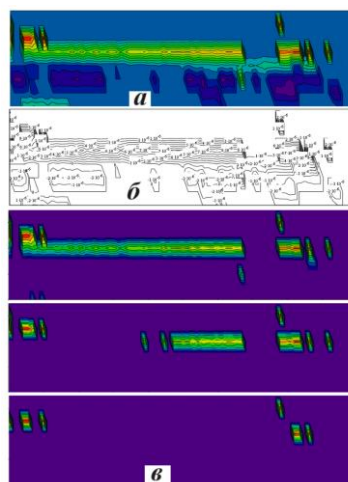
То же, что на рисунке 1 для образца со сварным швом, выполненным сваркой трением.
